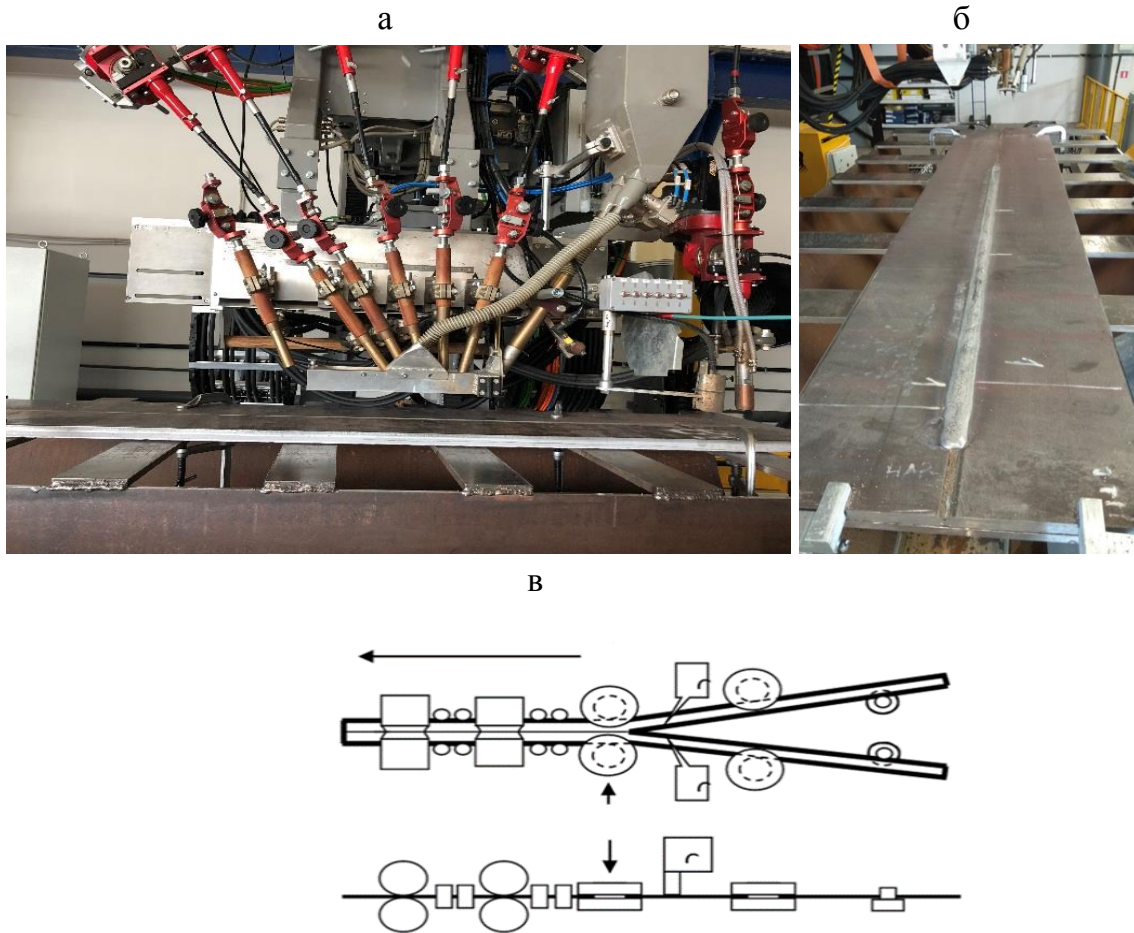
Вид лабораторного сварочного станда ИТЦ АО «ВМЗ» (а); сваренных пластин (б); общая схема лабораторного станда для исследования высокочастотной сварки (в).
